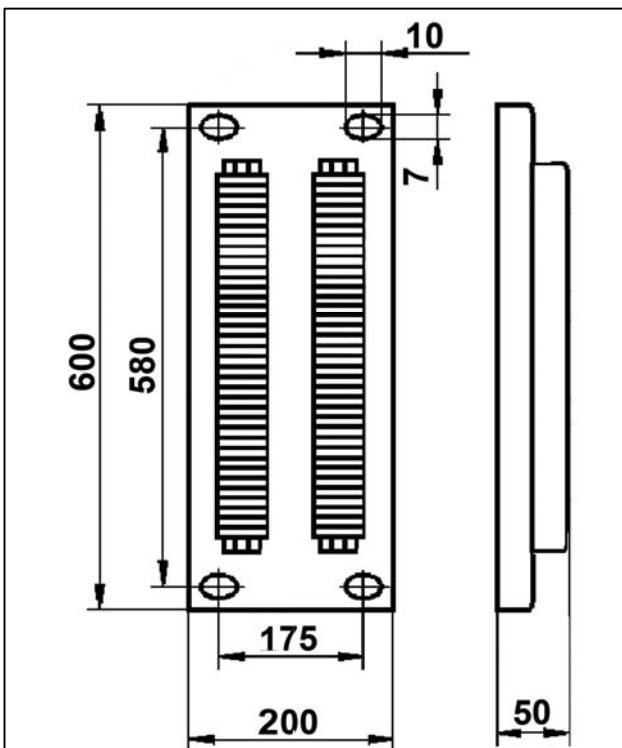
Габаритные и установочные размеры блока БК-2-У3
